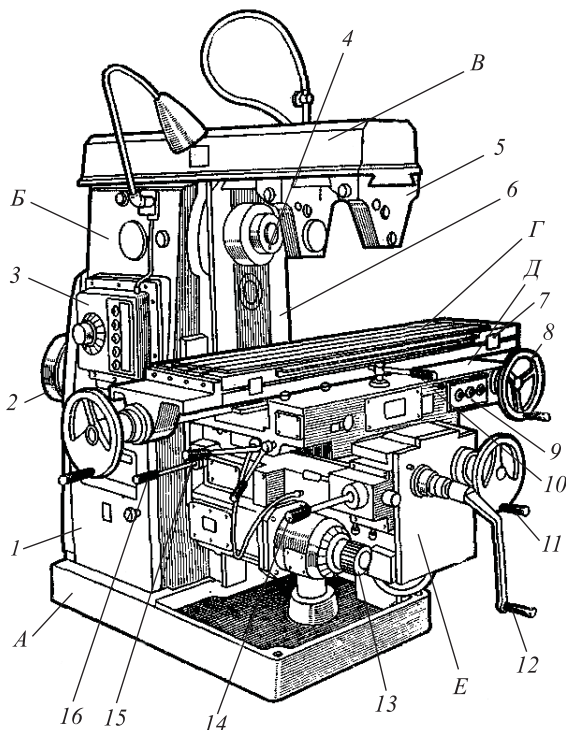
Горизонтальный консольно-фрезерный станок модели 6P82Г: А – основание; Б – станина; В – хобот; Г – стол; Д – салазки; Е – консоль
